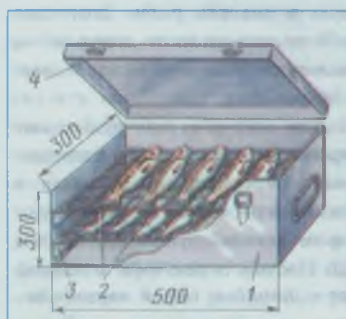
Коптильня переносная: 1 — корпус из нержавеющей стали; 2 — рамки с крупной сеткой, на которые раскладывается рыба; 3 — уголки-упоры; 4 — крышка.
